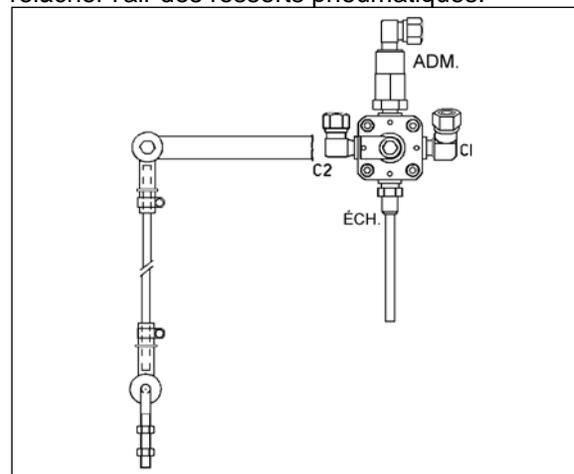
SOUPE DE COMMANDE DE HAUTEUR 16093
